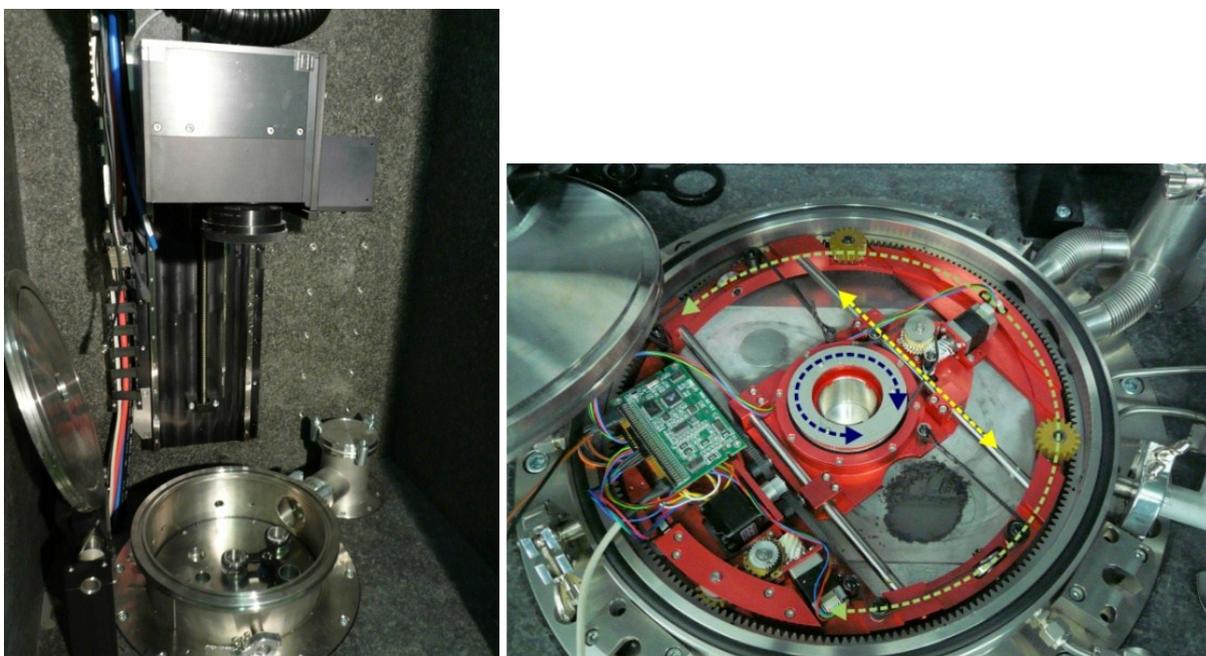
links: Sinteranlage zum Hochleistungsmikrosintern; rechts: Versuchsaufbau der Rakelvorrichtung mit Drehrakel (blau – Rotation der Rakel, gelb – lineare Aufzugbewegung, grün – Rotation der Rakelplattform)
